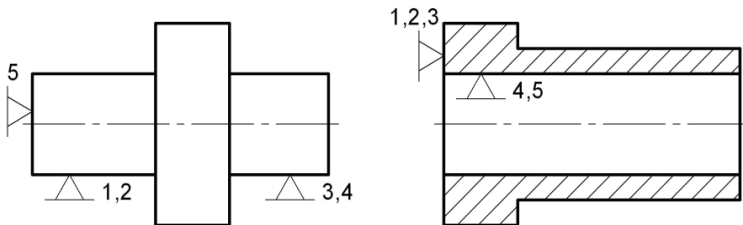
Схеми базування деталей типу тіл обертання:
